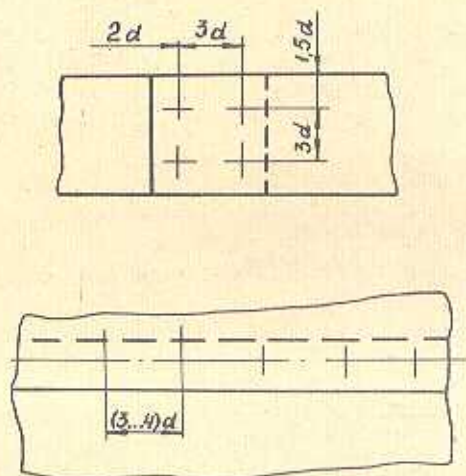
Рекомендуемые расстояния между сварными точками
